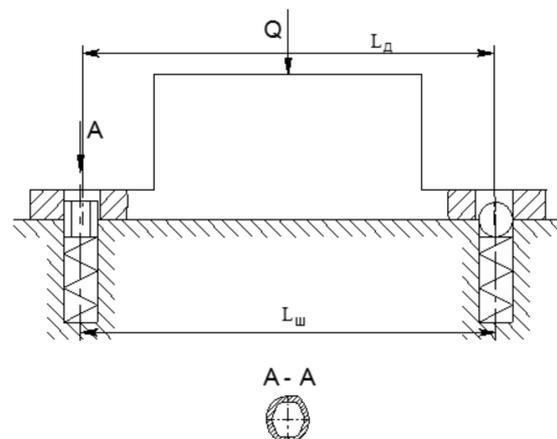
Установка заготовки на один срезанный палец и сферическую поверхность
